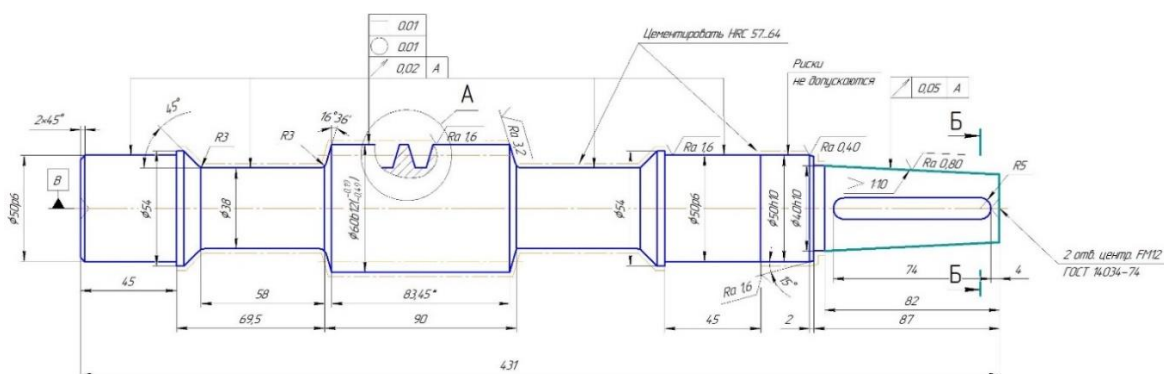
Ескіз обробки поверхонь на операції 050 Токарна з ЧПК
